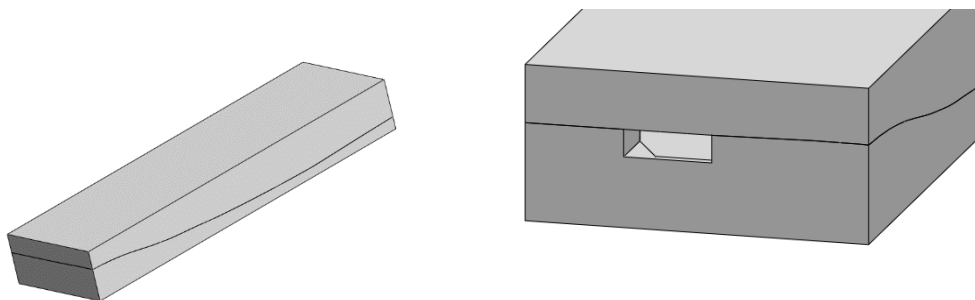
Aspeto final das cavidades do molde juntas e abertura para molde macho.
